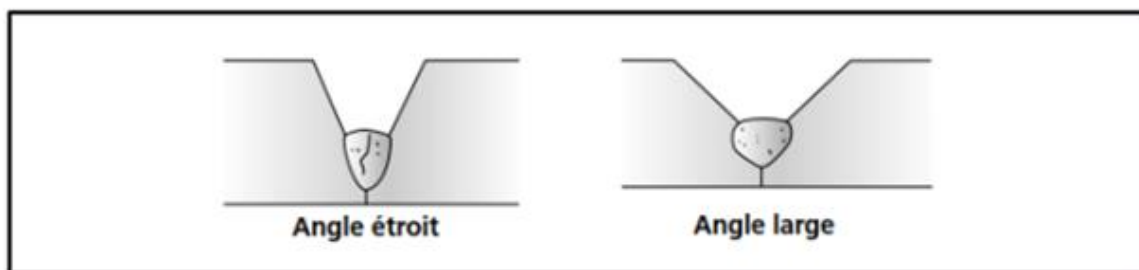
Fissuration à chaud d'un joint soudé (Réf. [R15])
